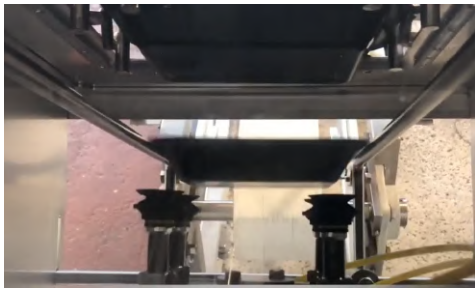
Máquinas de dispensa de embalagens, *Screw Denester*, da empresa *FEMC, Innovative Packaging Machinery* [16].
